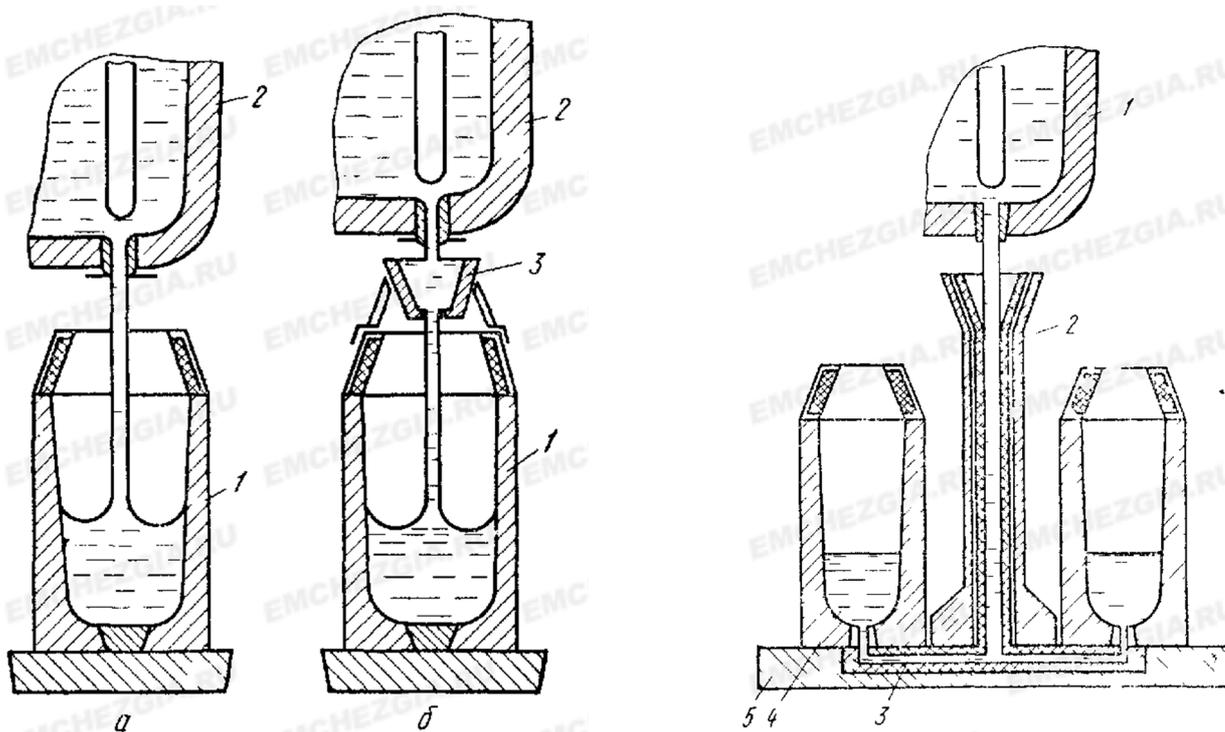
Разливка стали сверху (а,б) и сифонная разливка (в)
